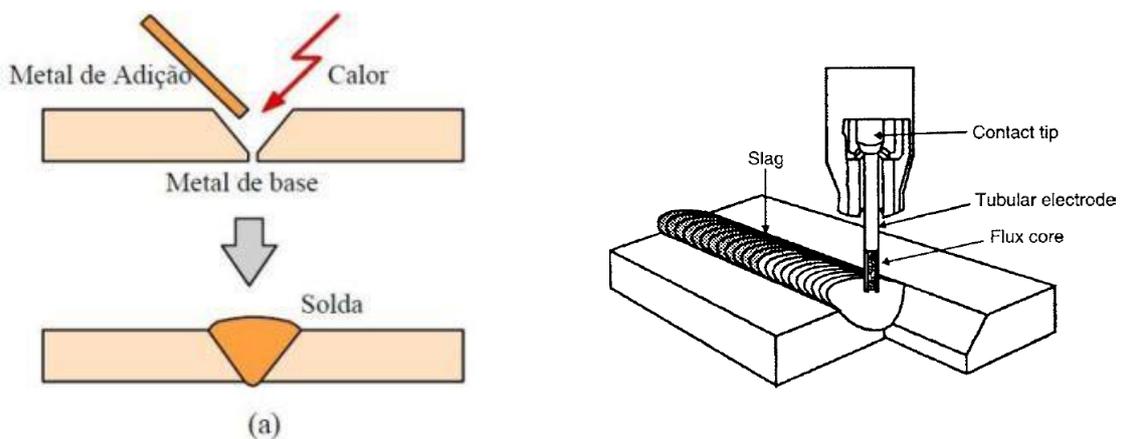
(a) Soldadura por brasagem [5]; (b) Soldadura autogénea [7]
